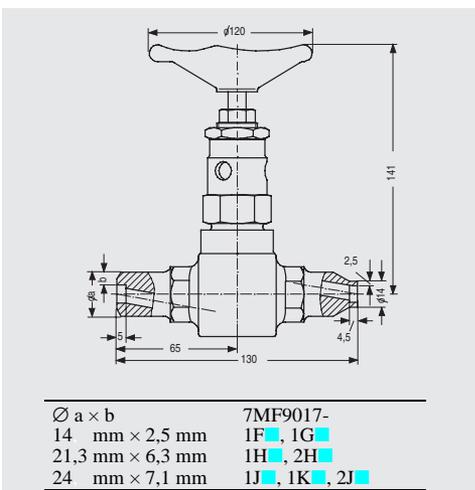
/135 Запорный вентиль 7MF9017-, размеры
